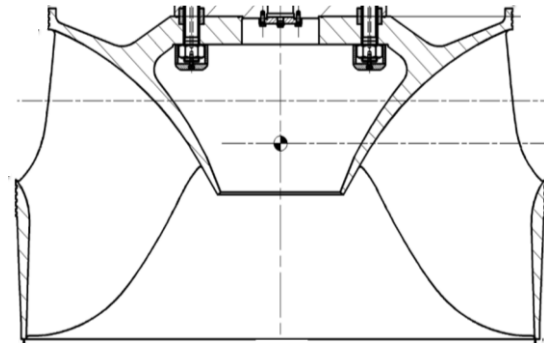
Desenho técnico de um rotor de turbina tipo Francis. Fonte: Própria.
